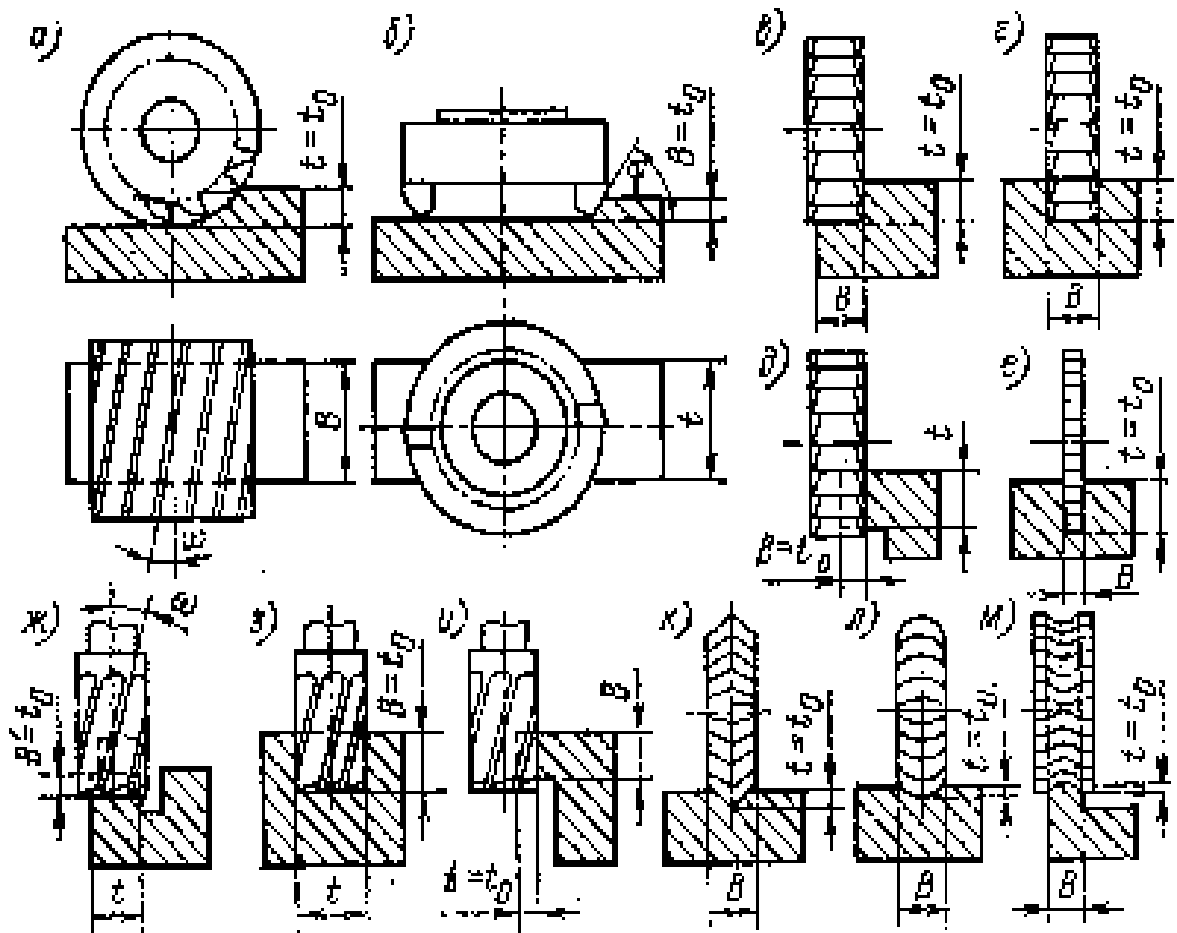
Позначення ширини фрезерування, глибини різання і глибини шару, що зрізається, при різних випадках обробки
